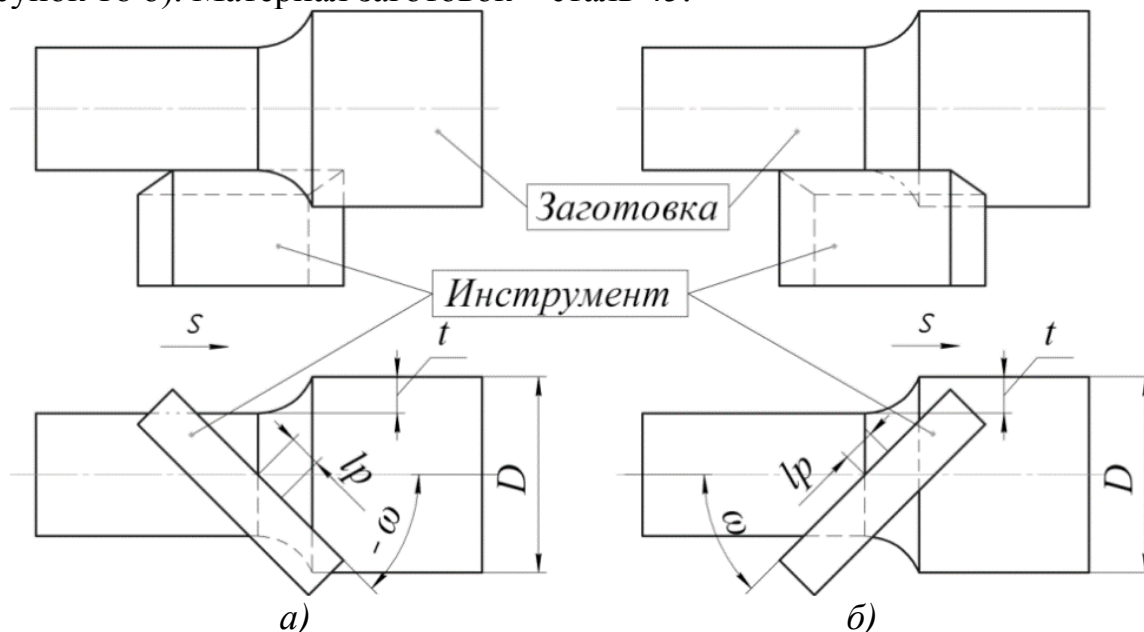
«Прямая» (а) и «обратная» (б) схемы резания безвершинными резцами
